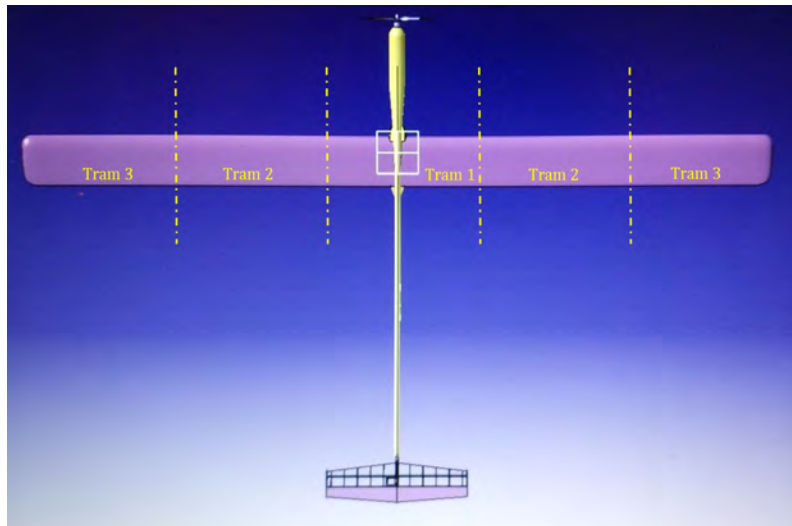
Vista en planta de l'avió i els trams d'ala
